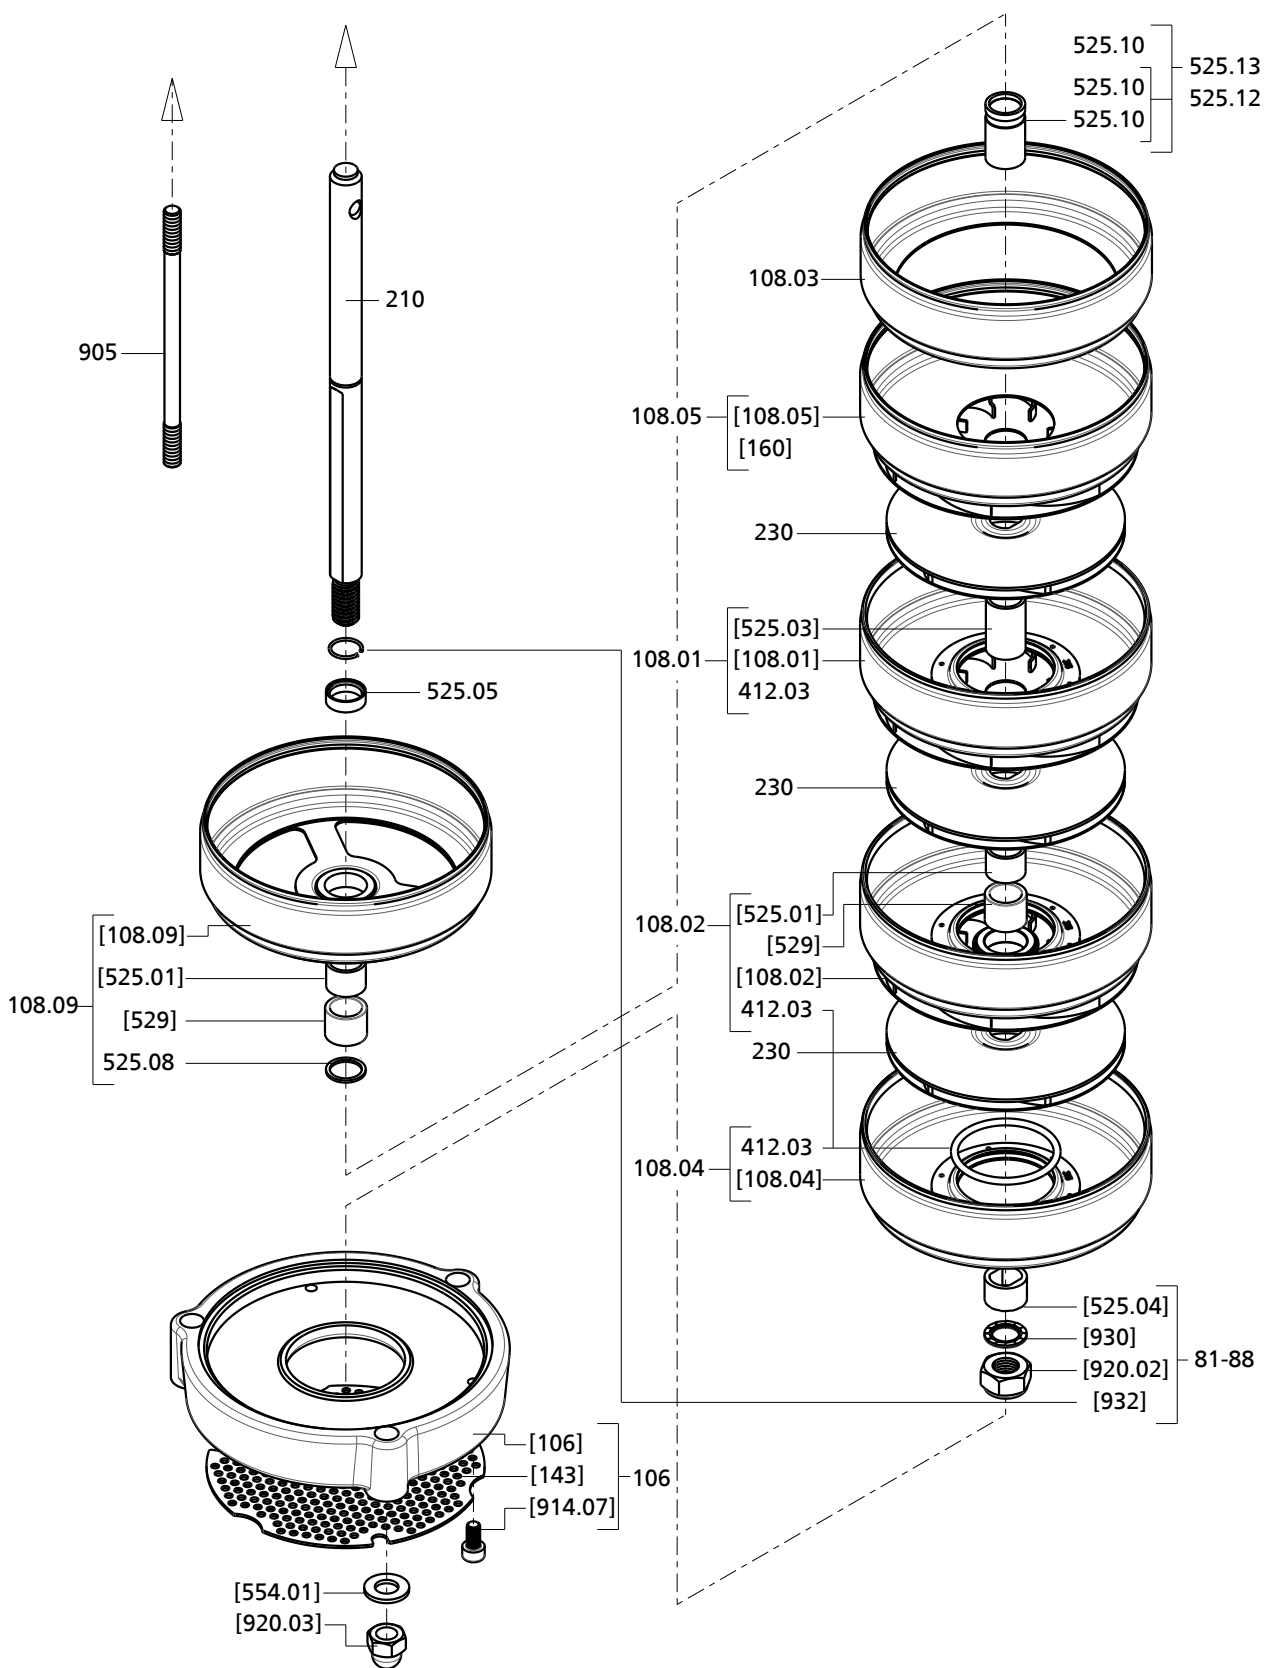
Покомпонентный сборочный чертеж проточной части [детали в квадратных скобках поставляются только в упакованных комплектах]
